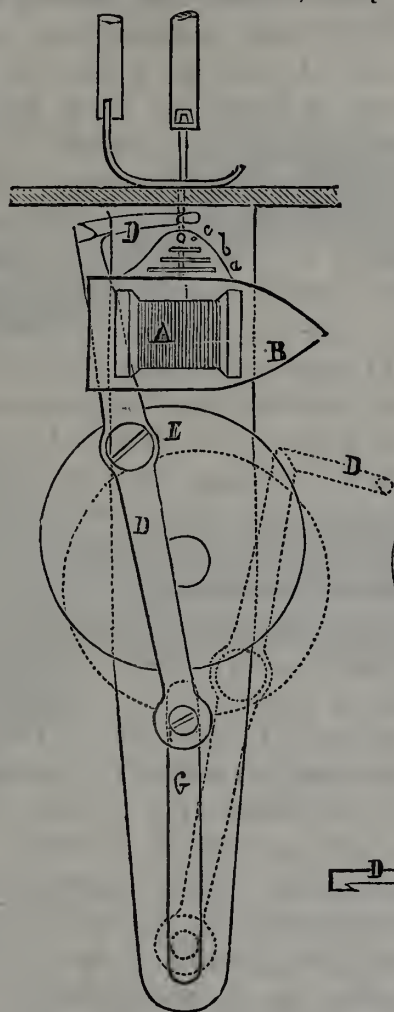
Machine Smith Stalrey et Cie. — Vue de face.
